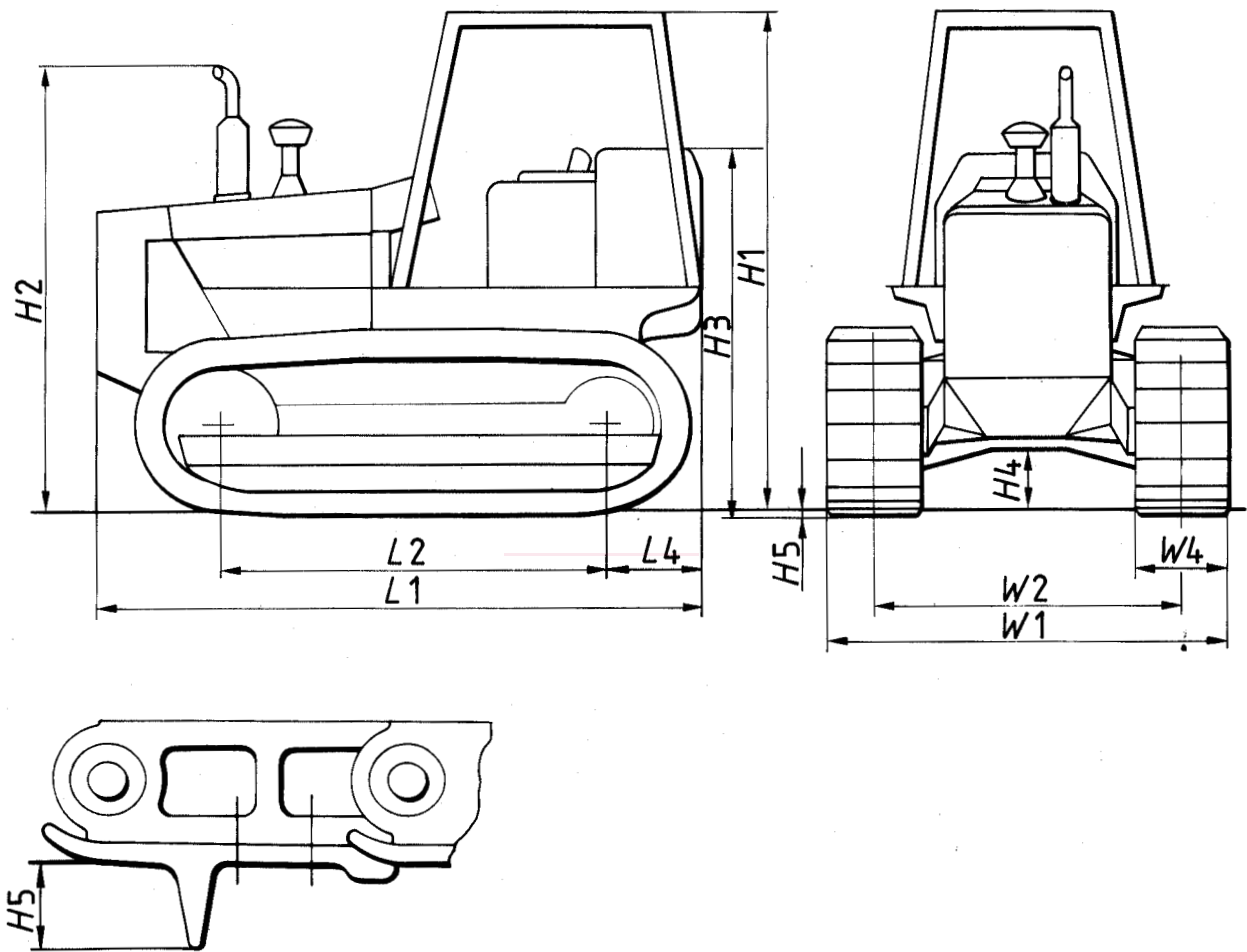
Dimensions de l'engin de base (tracteur sur chenilles)
